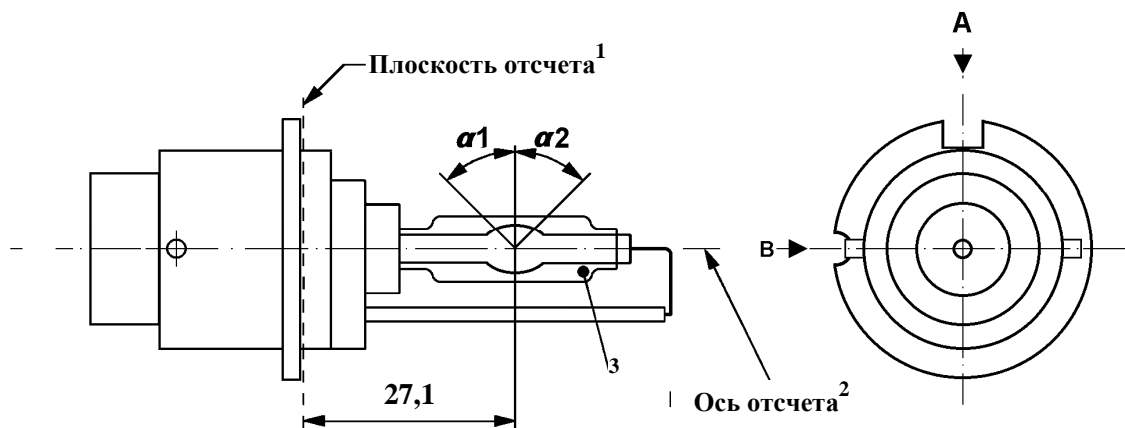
Категория D4S - Типовой газоразрядный источник света с соединительным устройством - Цоколь P32d-5
